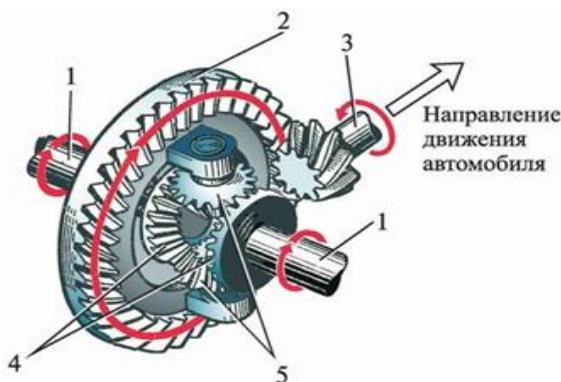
Главная передача с дифференциалом: 1 – полуоси; 2 – ведомая шестерня; 3 – ведущая шестерня; 4 – шестерни полуосей; 5 – шестерни-сателлиты
